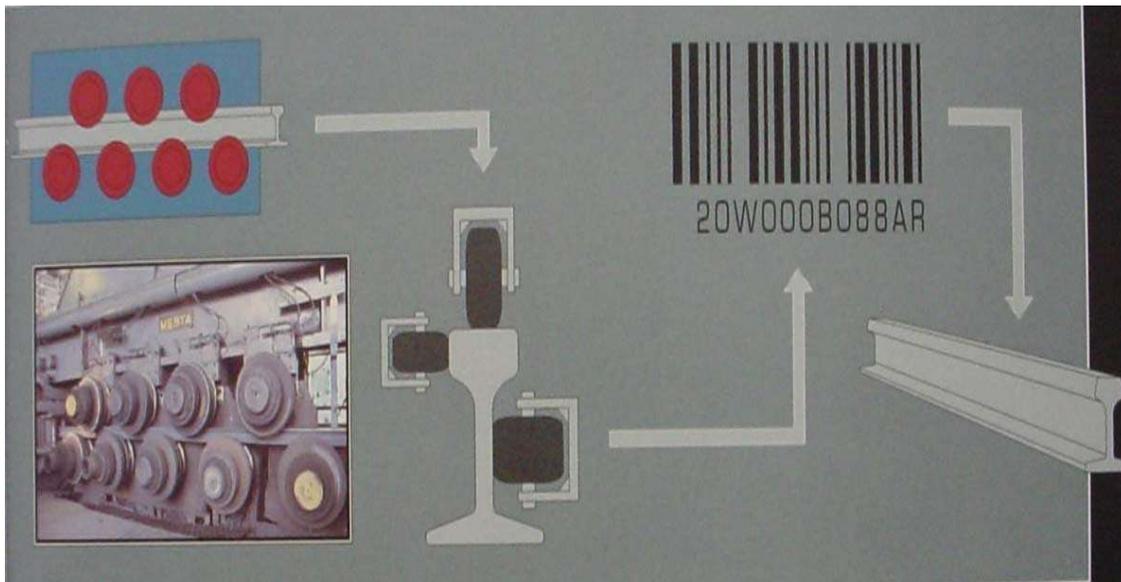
Enderezador de rodillo, inspección en-línea, etiqueta de código de barras
